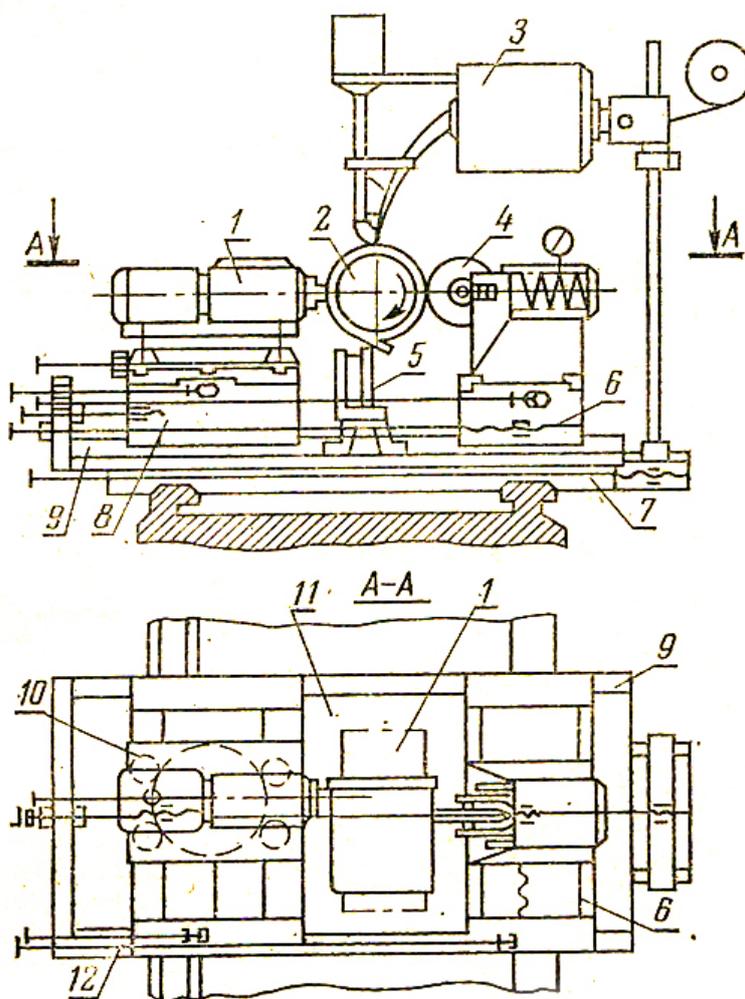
Схема установки для наплавки цилиндрических деталей под флюсом с одновременным фрезерованием и накаткой роликом: 1 — фрезерная головка; 2 — обрабатываемая деталь; 3 — наплавочная головка; 4 — накатной ролик; 5 — шлакоудаляющее устройство; 6 — суппорт накатной головки; 7 — карета токарного станка; 8 — суппорт фрезерной головки; 9 — поперечные направляющие; 10 — каретка с подъемными винтами; 11 — несущая плита; 12 — продольные направляющие
